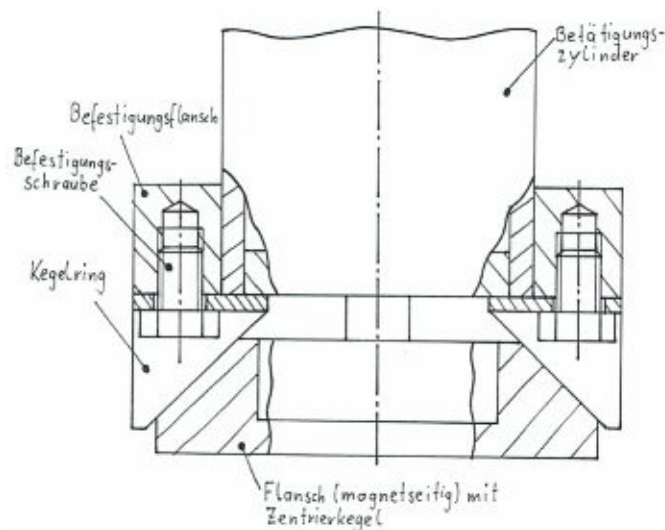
Zentrierung mittels Kegelring am Zylinderflansch
